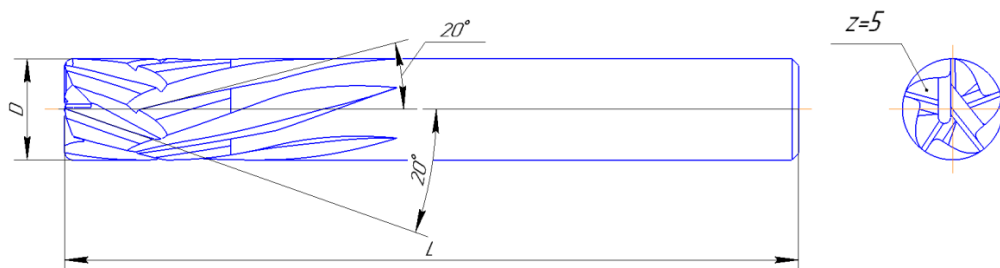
Эскиз концевой твердосплавной фрезы «РК 686»
